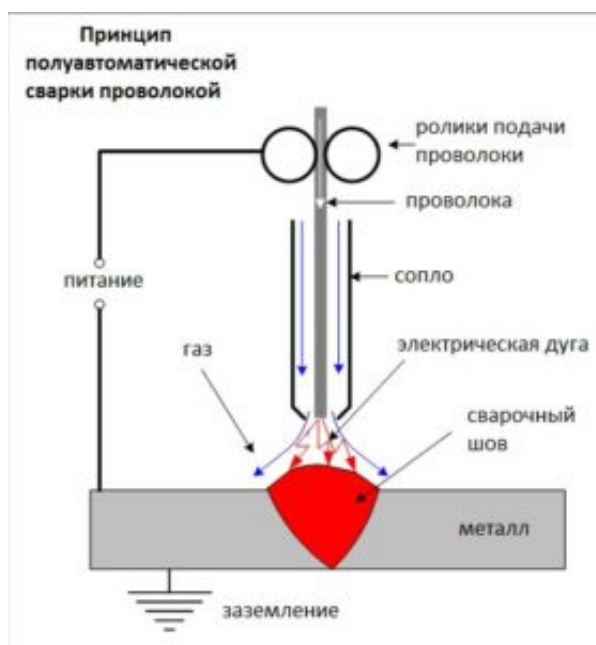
Схемой полуавтоматической сварки
